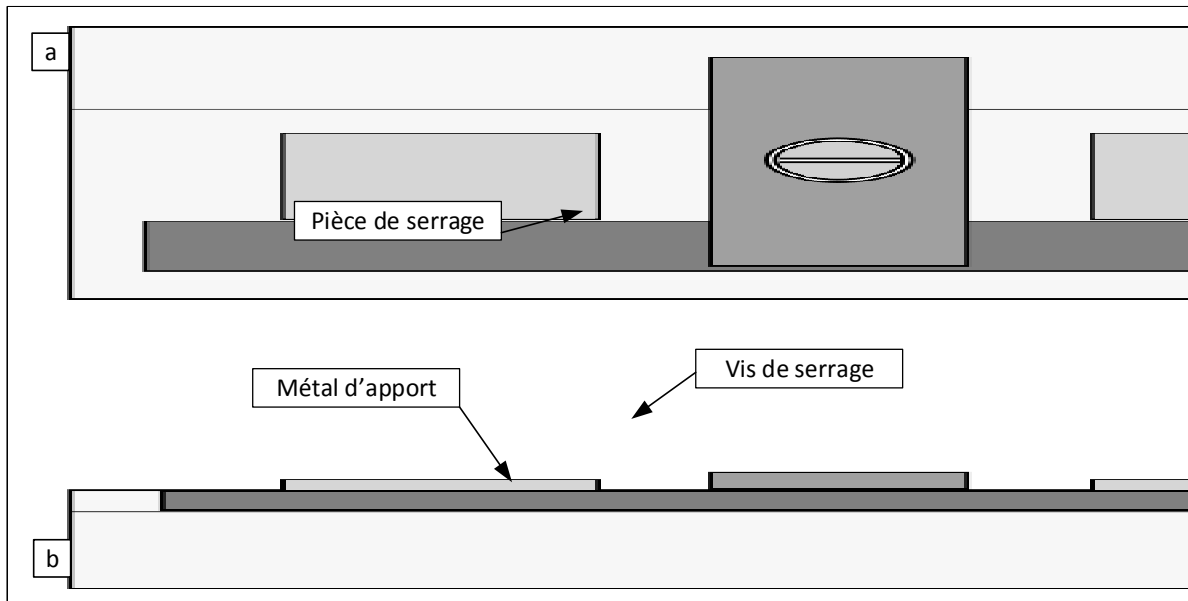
Gabarit de montage des assemblages brasés : (a) vue de dessus, (b) vue de côté
